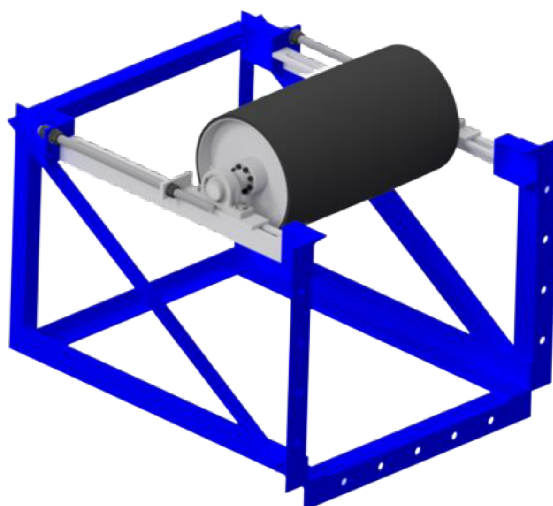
Pohon dopravníku a detail jeho upevnění ke konstrukci
